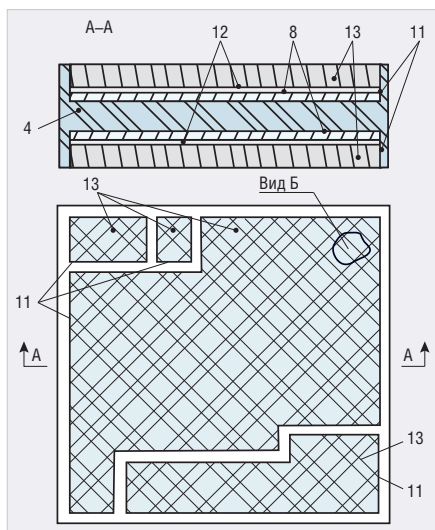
Области металлизации топологического рисунка керамической пластины (А–А – вид сверху) и керамическая пластина с адгезионным слоем из алюминия и никеля и слоем меди (вид Б – в сечении)
